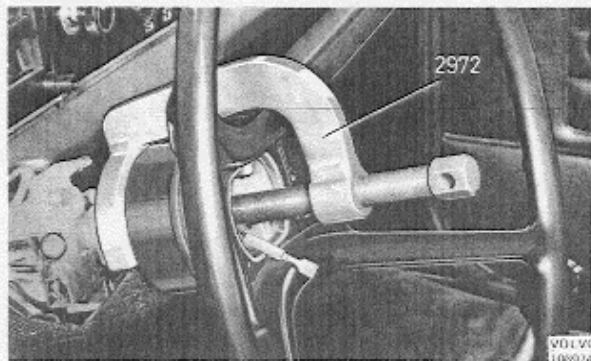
Ausbau des Lenkrades, bis einschl. Bauj. 1972
